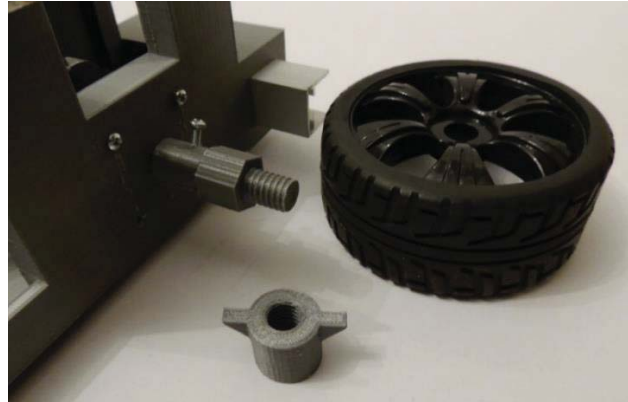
Pieza de conexión del rotor del motor con la rueda de la plataforma
